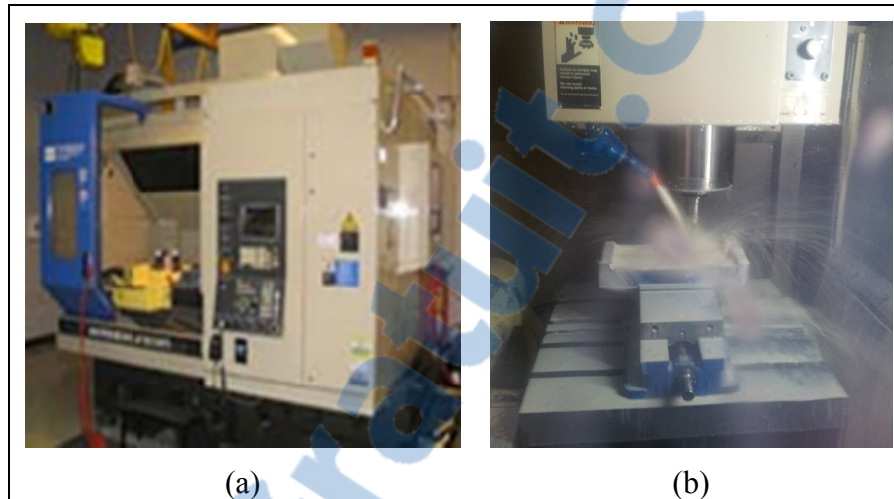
(a) Machine-outil (b) Montage utilisé lors de l'usinage.
